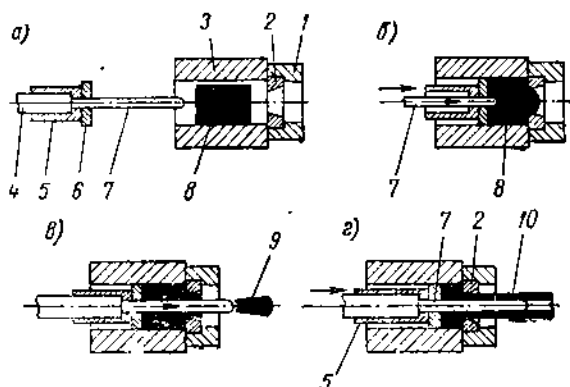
Схем: технологии прессования трубы прямым методом: а — момент загрузки заготовки; б — момент начала прошивки; в — конец прошивки; г — выдавливание
